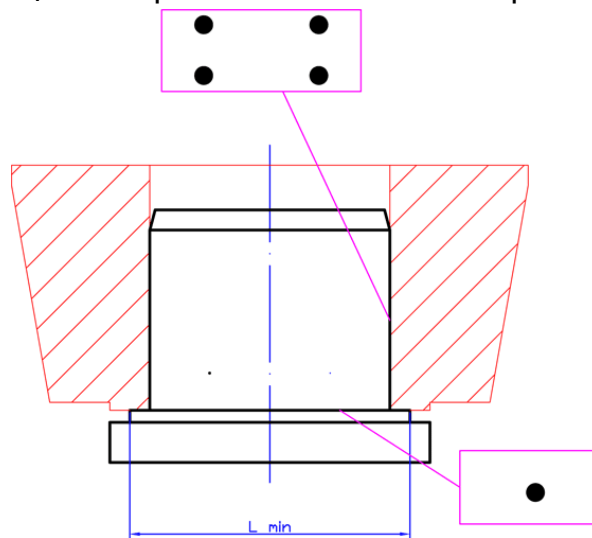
Базирование по длинной конической поверхности схема 1 - основной базирющей поверхностью является торец
